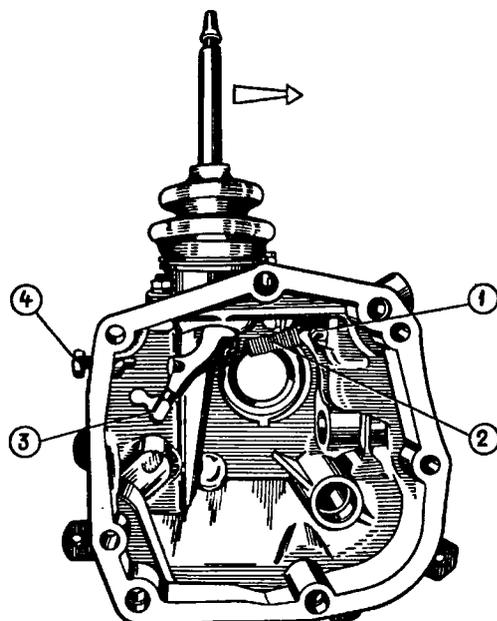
Внутренний вид задней крышки коробки передач: 1 - винт с ушком крепления оттяжной пружины рычага переключения передач; 2 - оттяжная пружина рычага; 3 - рычаг переключения передач; 4 - винт ограничения поперечного хода рычага. Стрелкой указано направление, в котором нужно переместить рычаг, чтобы вывести его из зацепления с головками штоков переключения передач и снять заднюю крышку коробки передач
